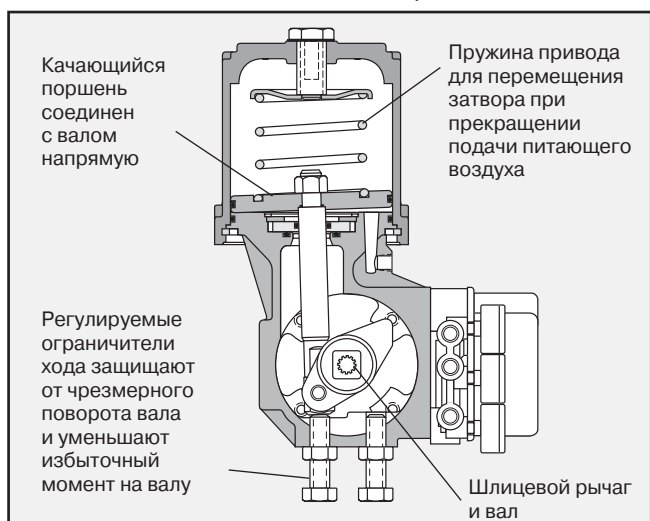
Поршневой привод с вращательным движением выходного вала с пружиной
